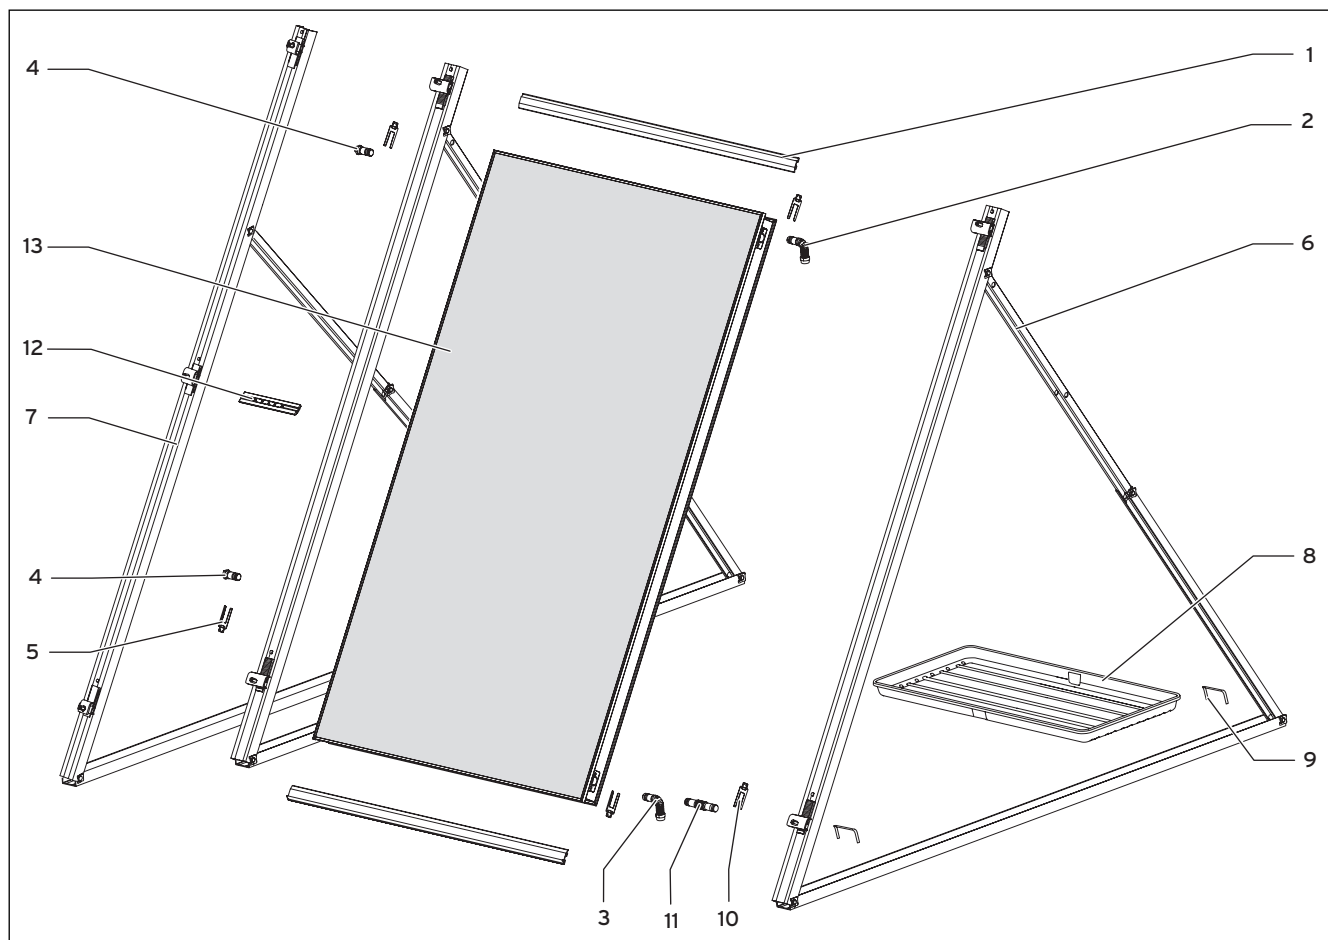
Einbauset für vertikale und horizontale Flachdachmontage (hier: Vertikaler Kollektor)
